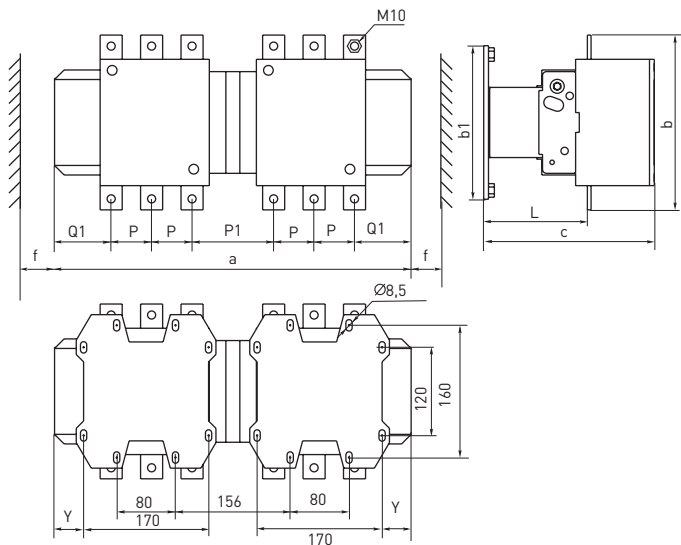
Габаритные и установочные размеры реверсивного КТЭ-2 (400А; 500А)
